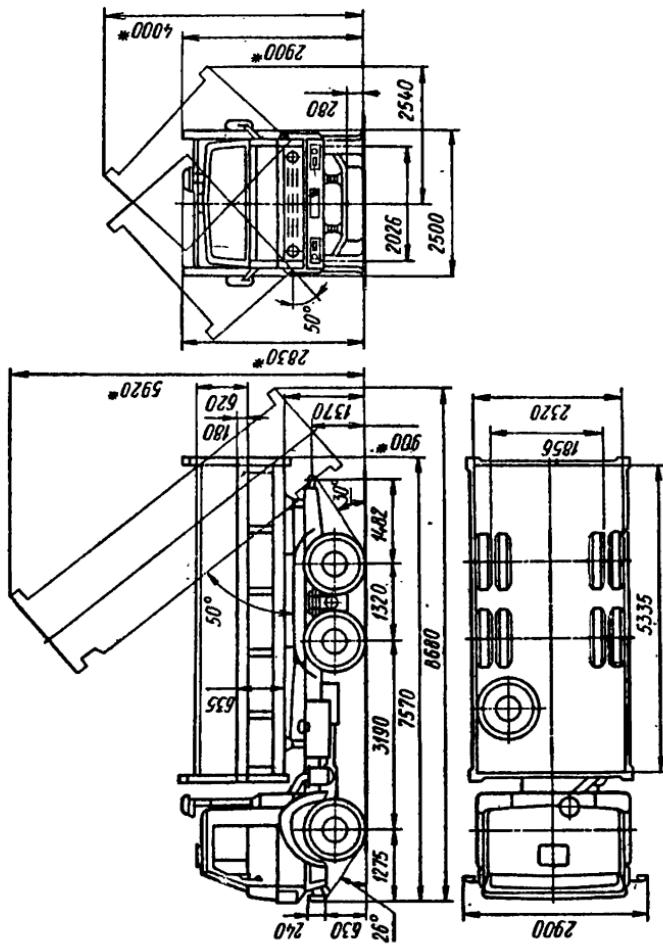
Габаритные размеры самосвала КамАЗ-5511
